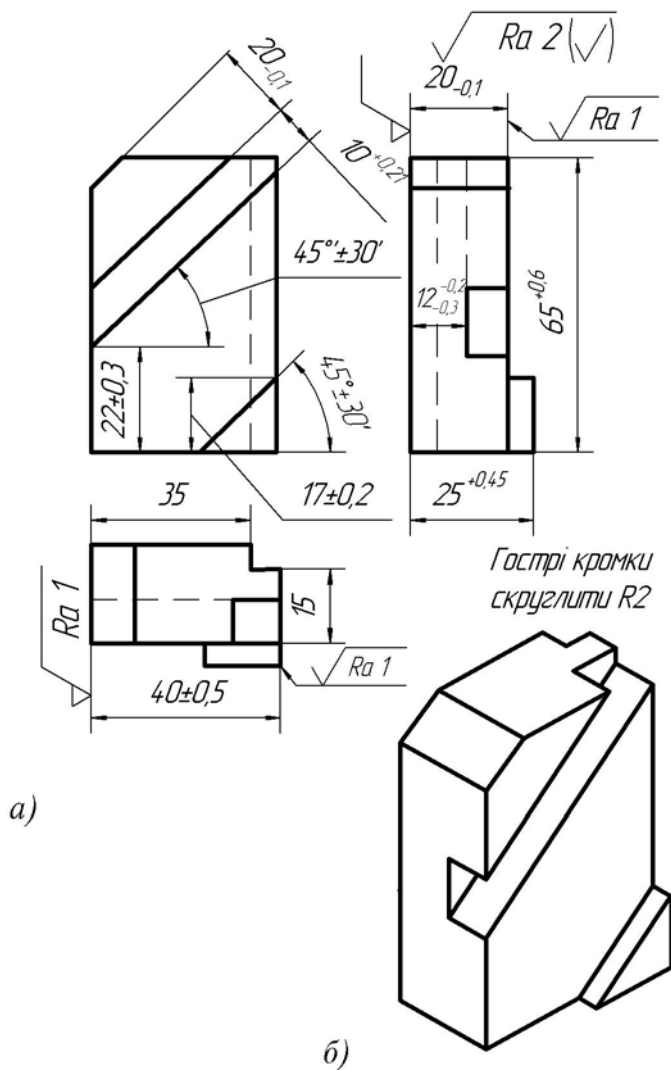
Приклад робочого кресленика деталі, форма якої визначається трьома зображеннями
